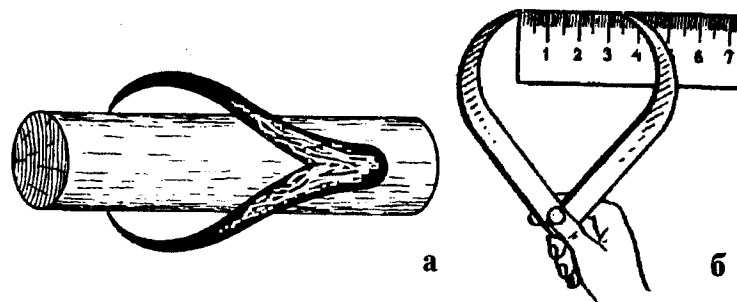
Контроль диаметра круглой детали: а — измерение размера кронциркулем; б — отсчет размера по линейке
